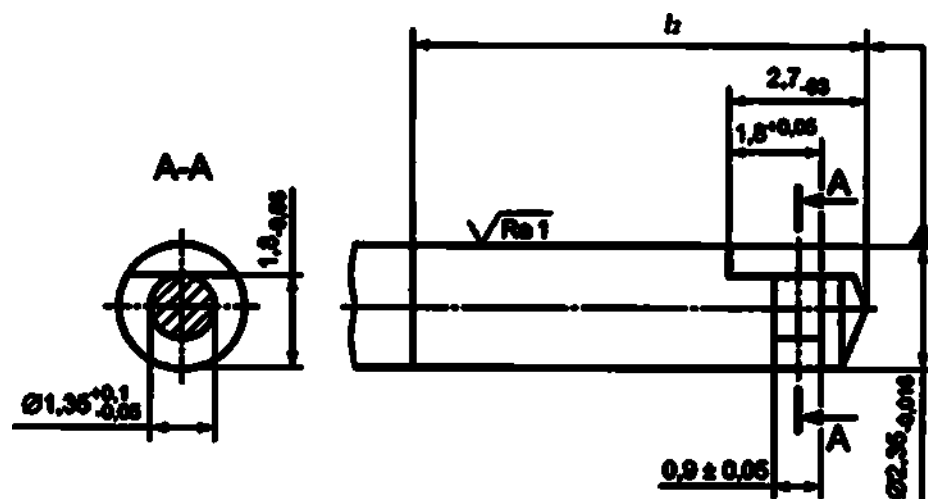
Размеры, допуски и шероховатость поверхности для хвостовика типа 1
